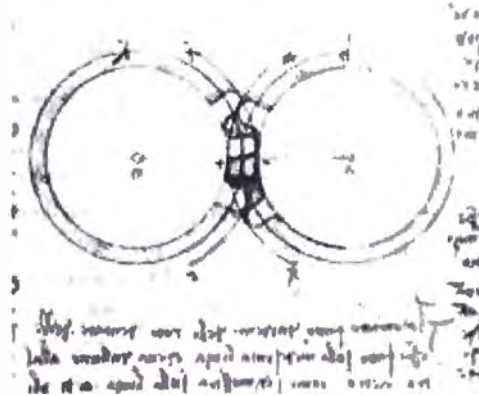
Engranaje diseñado por Leonardo Da Vinci
